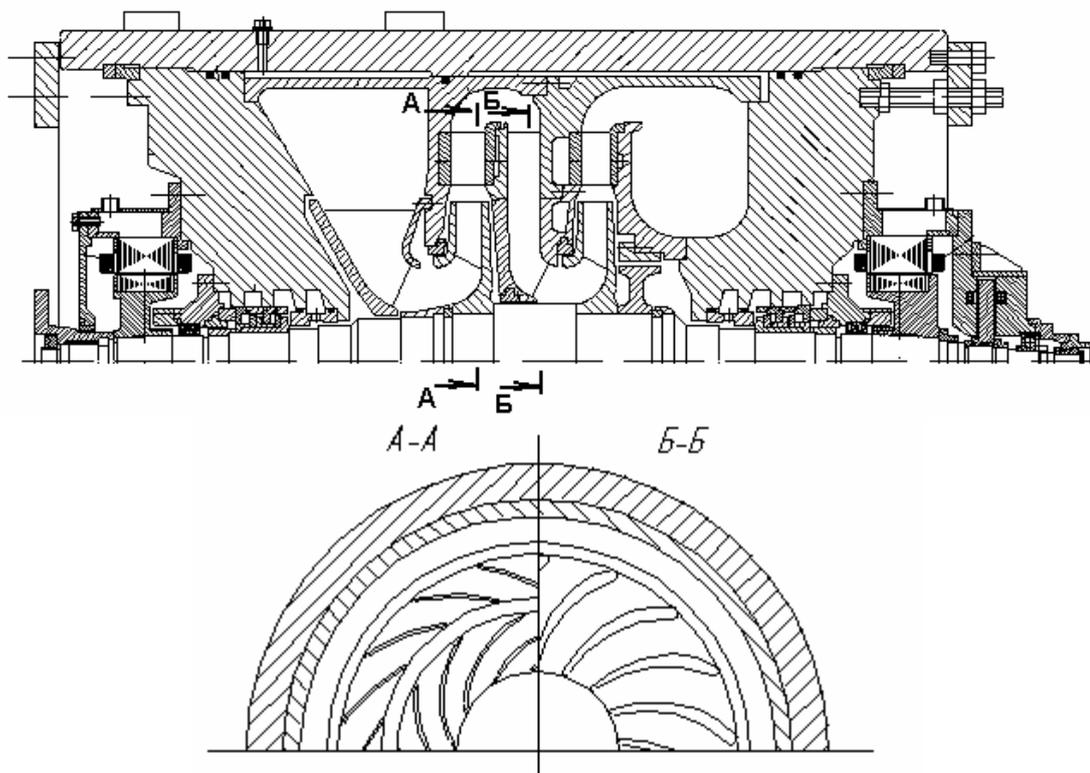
Двухступенчатый центробежный компрессор высокого давления.
